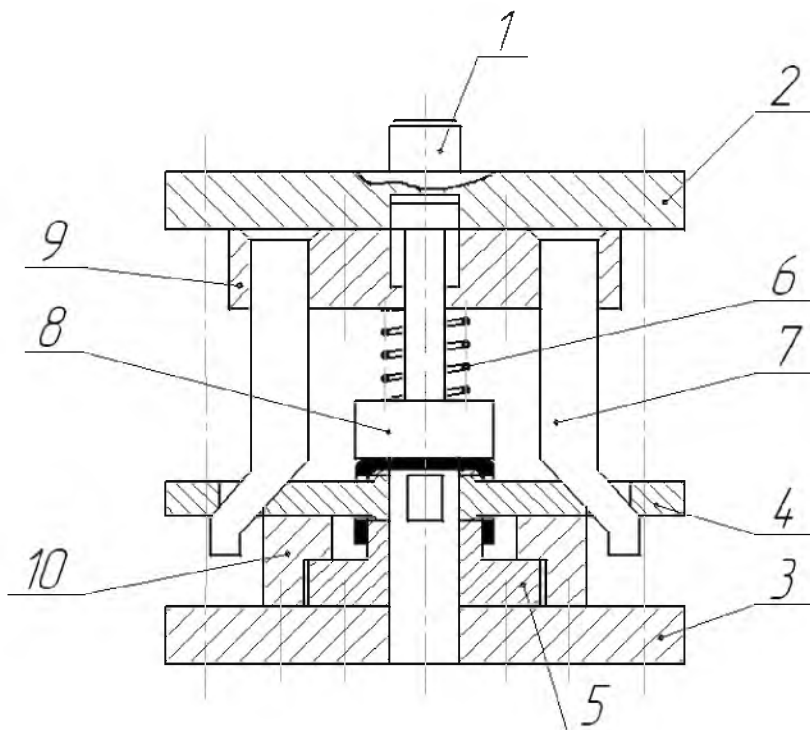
Схема клинового штампа для пробивки боковых отверстий
